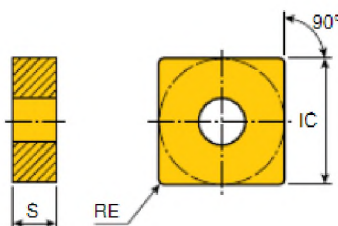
Пластина SNMG120408. CVD покриття : TT8115B
